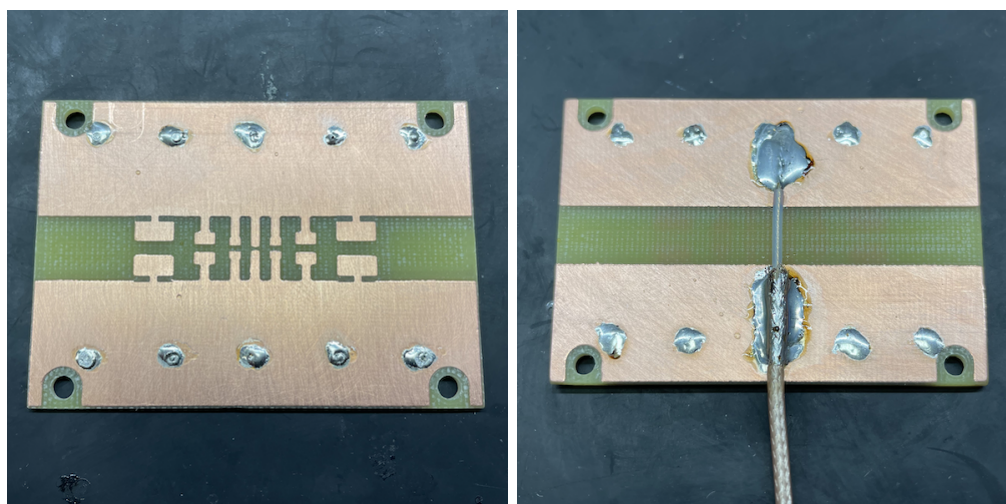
Přípravek DCCapSens – Přední a zadní část
